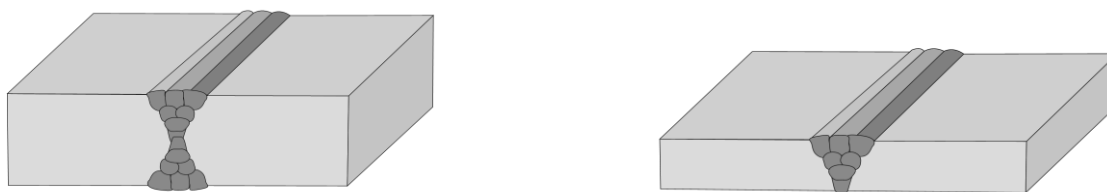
Виды сварных швов: DV-шов (а); V-шов (б)
